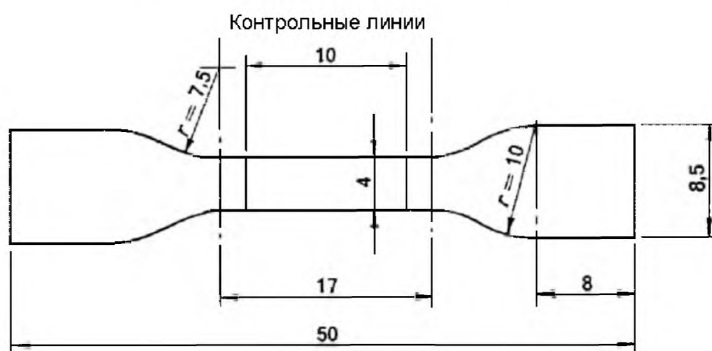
Испытуемый образец небольшого размера в виде двусторонней лопатки
